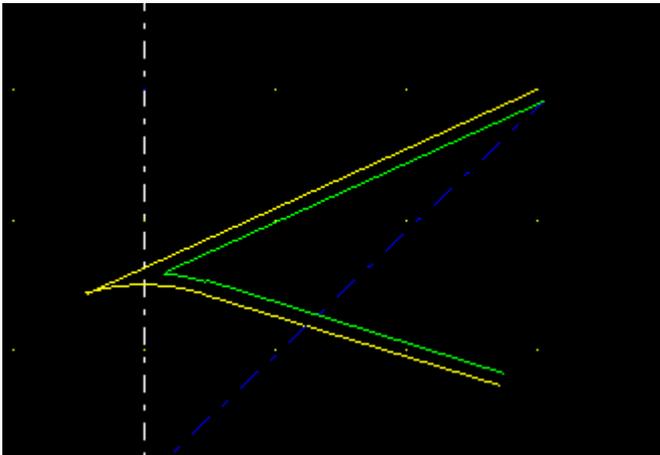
Richtige Ausgabe durch Verkleinerung des Werkzeugdurchmessers
